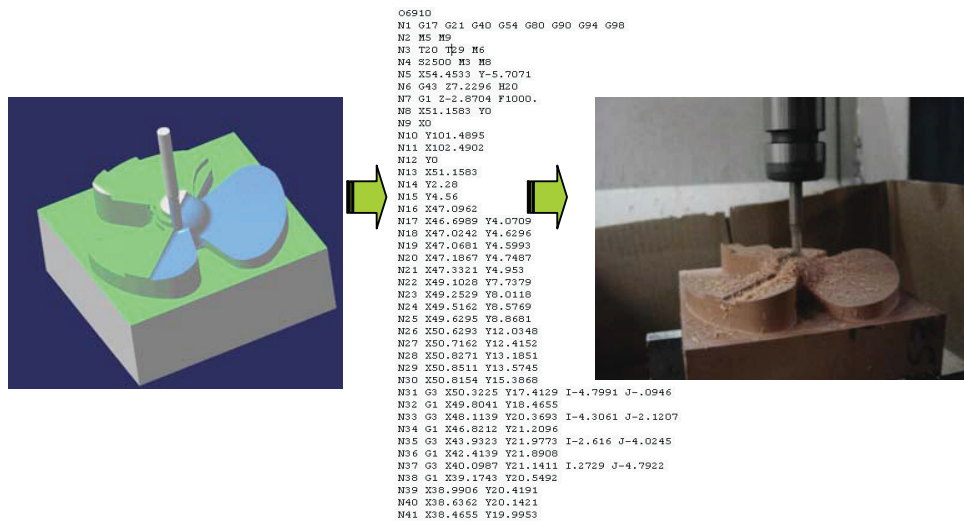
Usinagem Virtual- Programa gerado para a máquina CNC - Usinagem Real.
